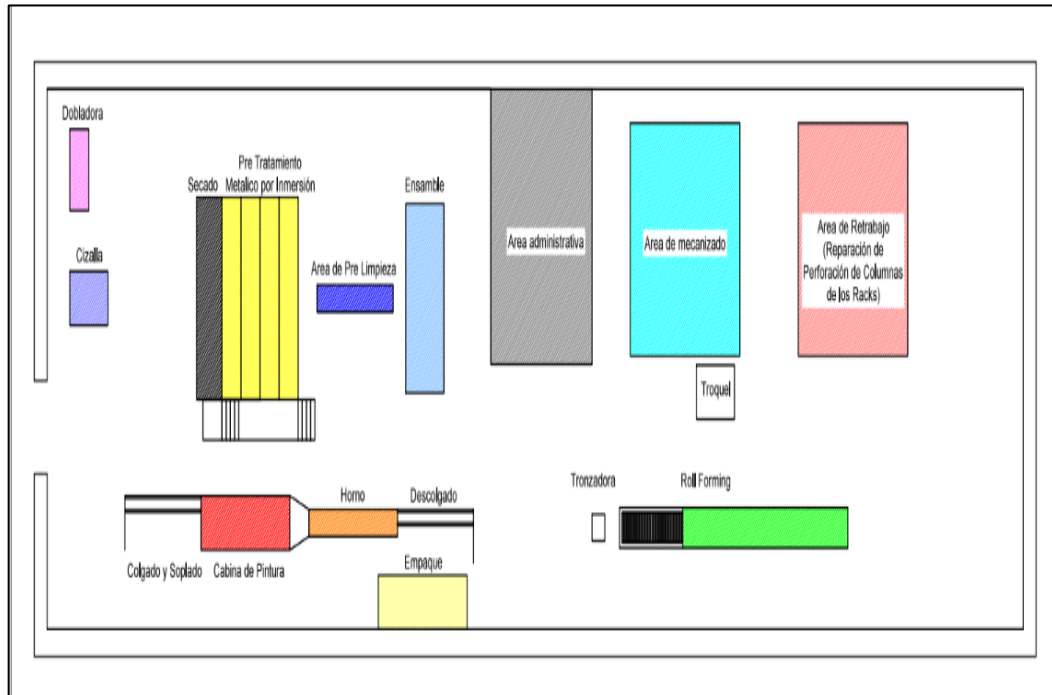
Layout actual de la empresa RubikAssembly C.A.
